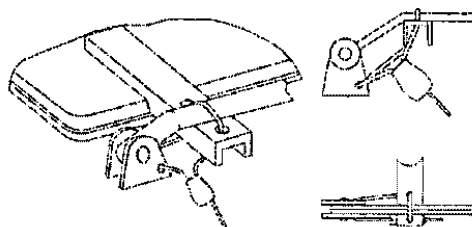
Схема установки универсального ЗПУ с длиной каната 300 мм на запорно-блокировочном механизме загрузочного люка вагона-хoppers для перевозки зерна модели 19-752
